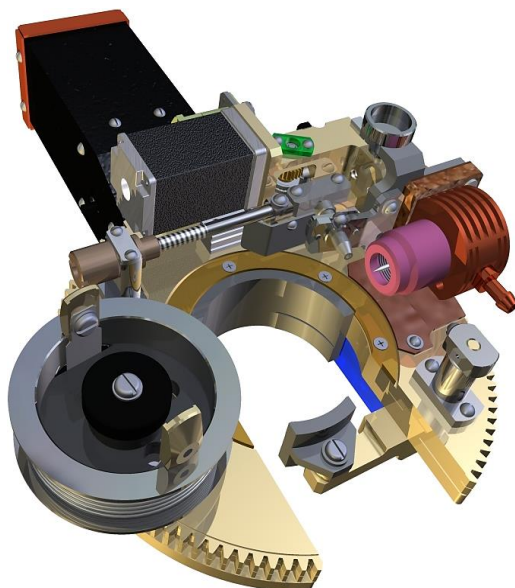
Общий вид сварочной головки на этапе 3D-моделирования
